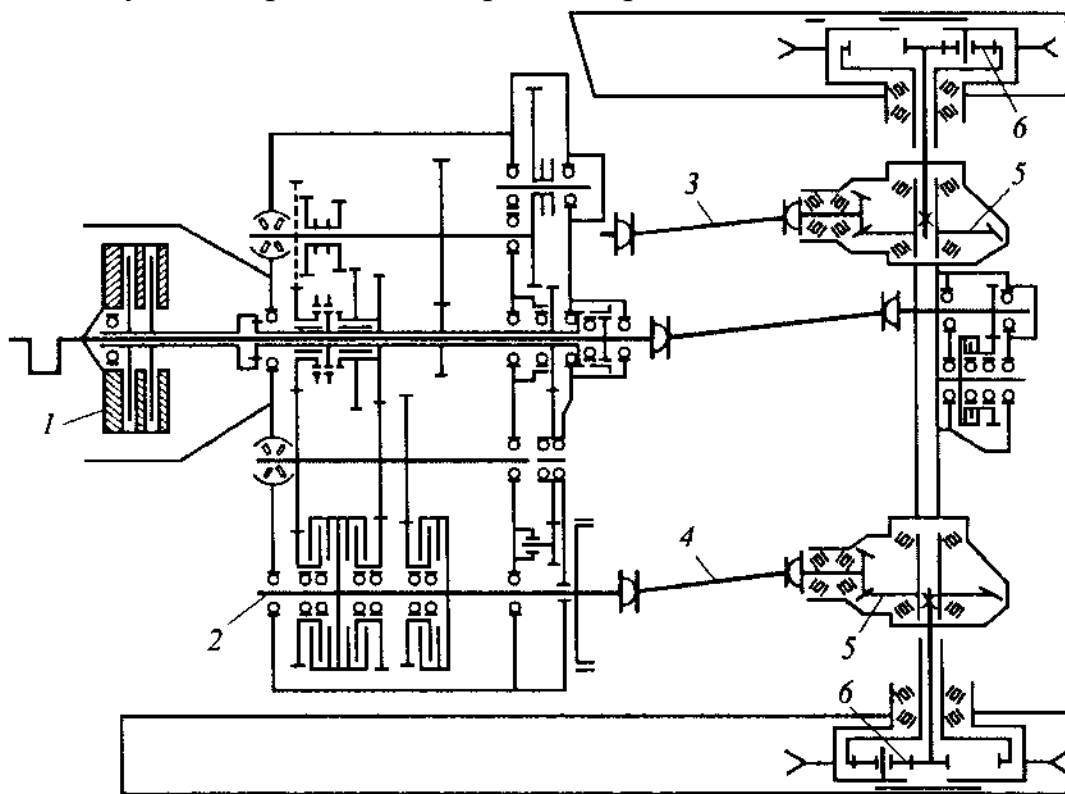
Схема механізму повороту гусеничного трактора Т-150:
